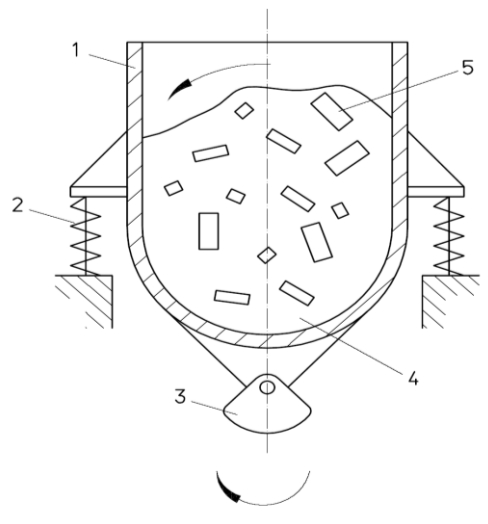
Принципова схема процесу віброабразивної обробки
